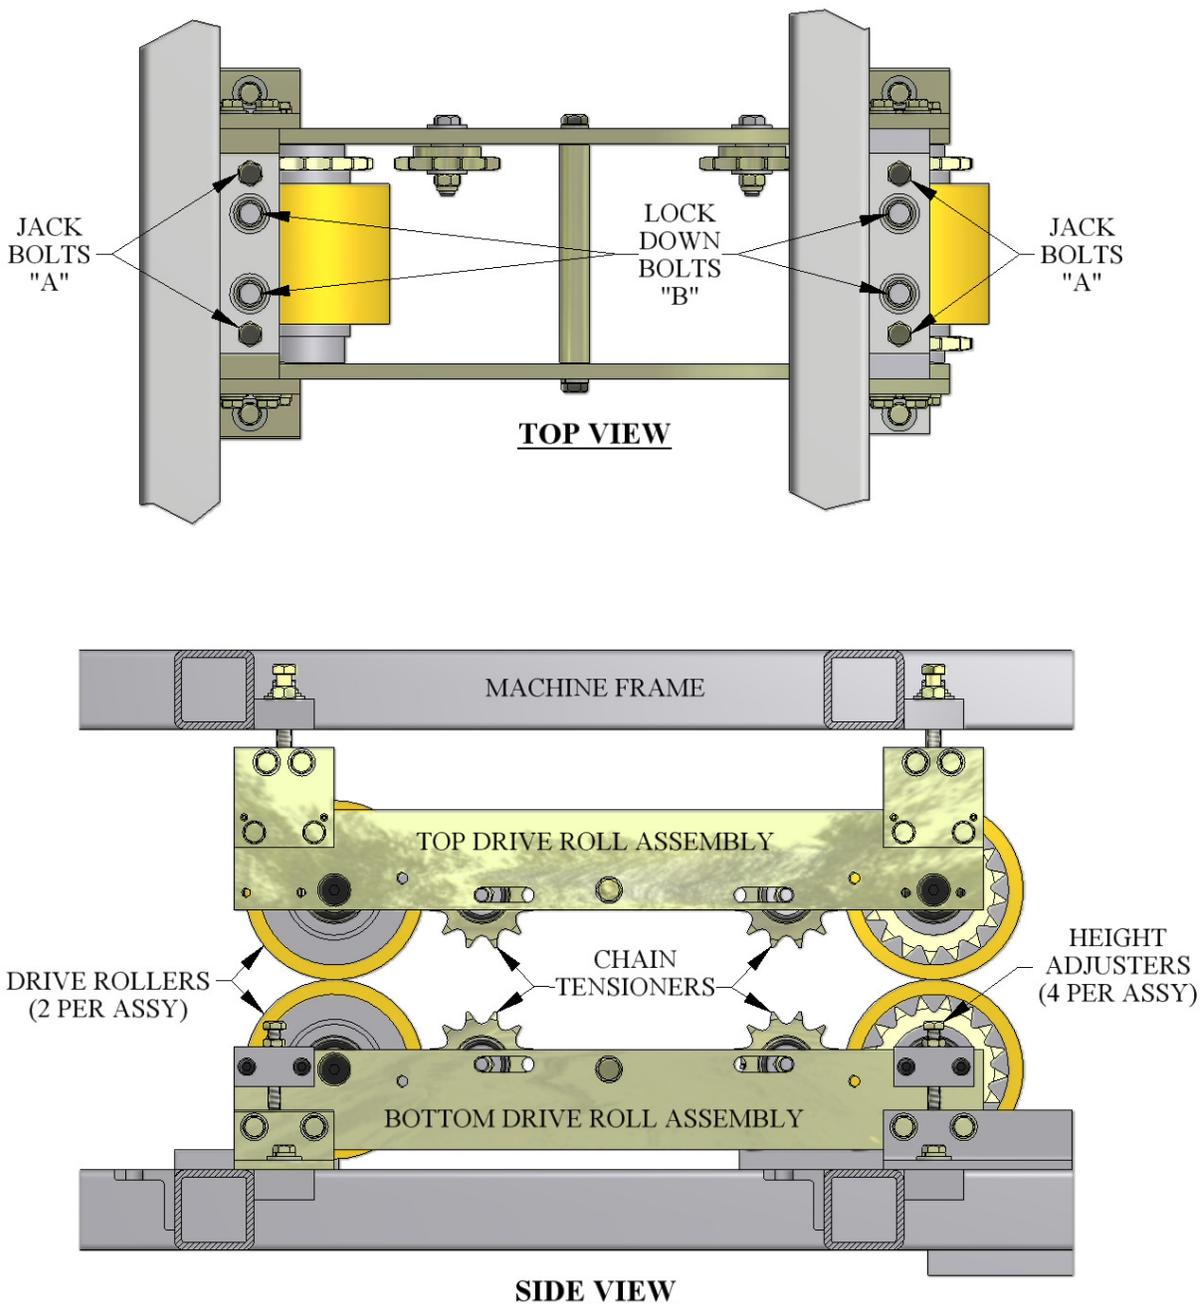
Vista del Ensamble del Rodillo de Impulso
